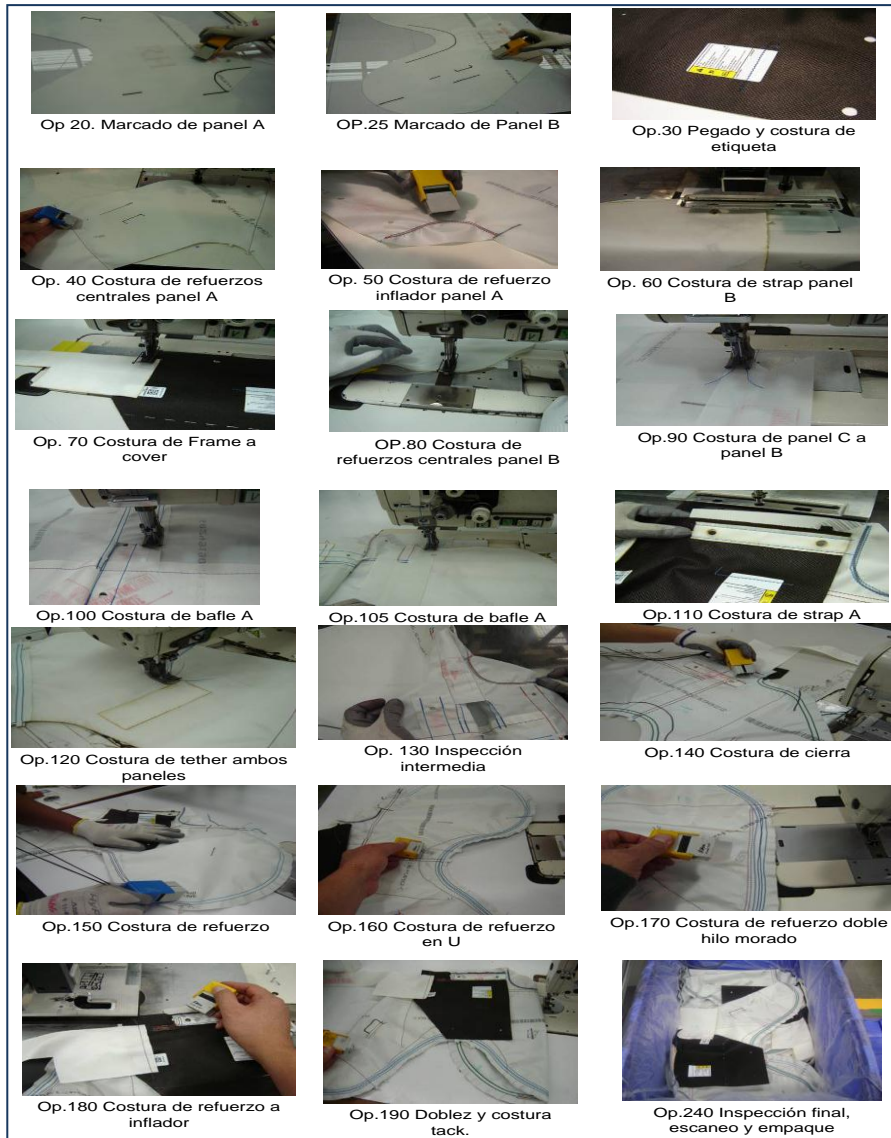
1 Descripción del proceso de manufactura de bolsa de aire
